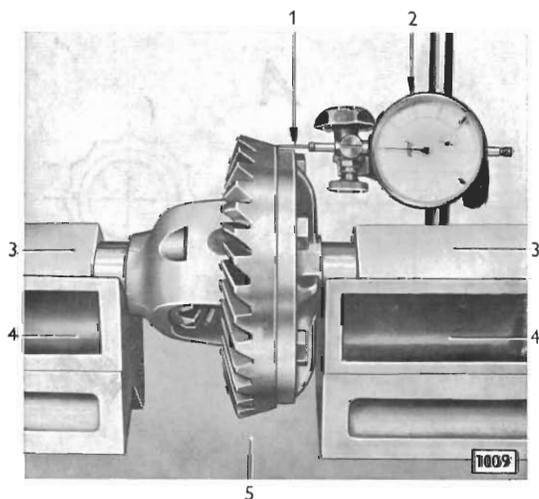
Tellerrad am Ausgleichgehäuse auf Seitenschlag prüfen
